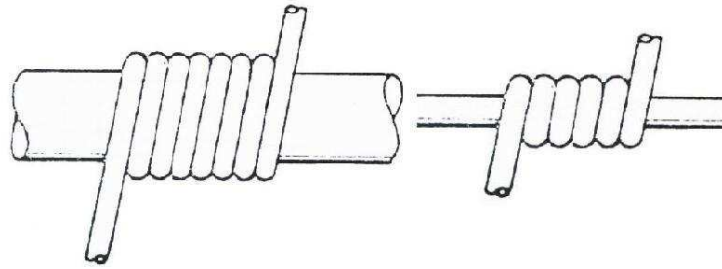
Esquema de la prueba de enrollado de alambre de acero
